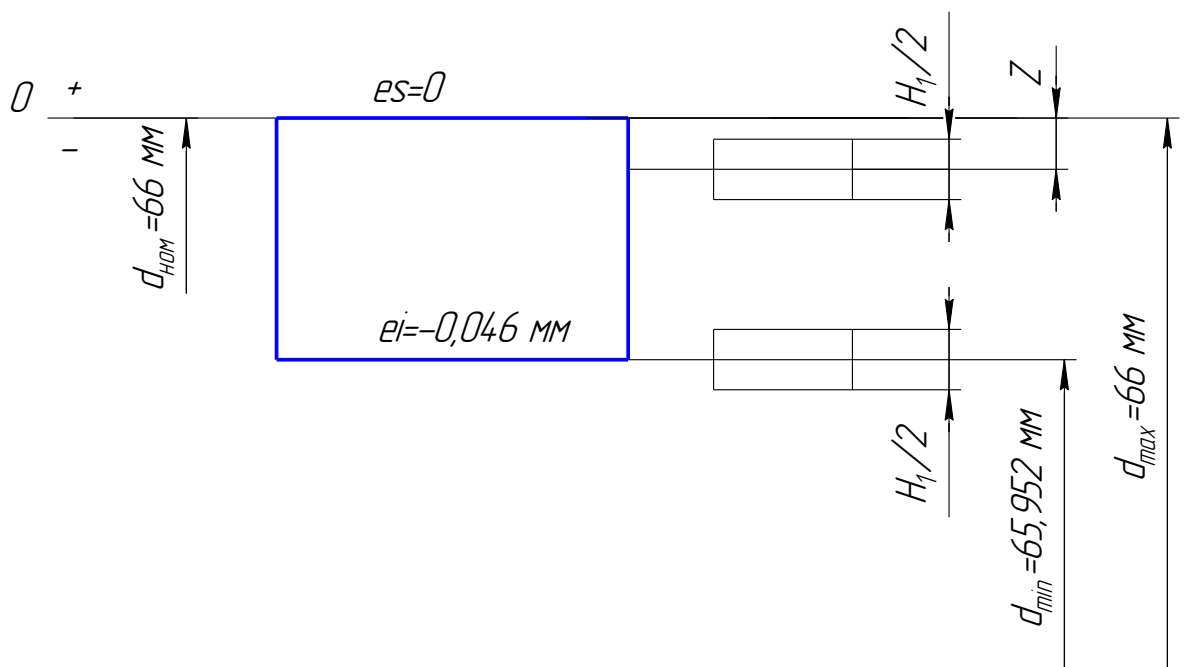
Схема розташування допусків робочих поверхонь скоби для контролю розміра  $\varnothing 66h8(-0,046)$
